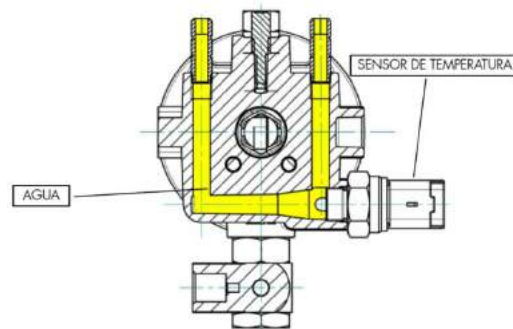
Regulador de presión. Corte longitudinal. (Fuente: BRC Gas Equipment)
